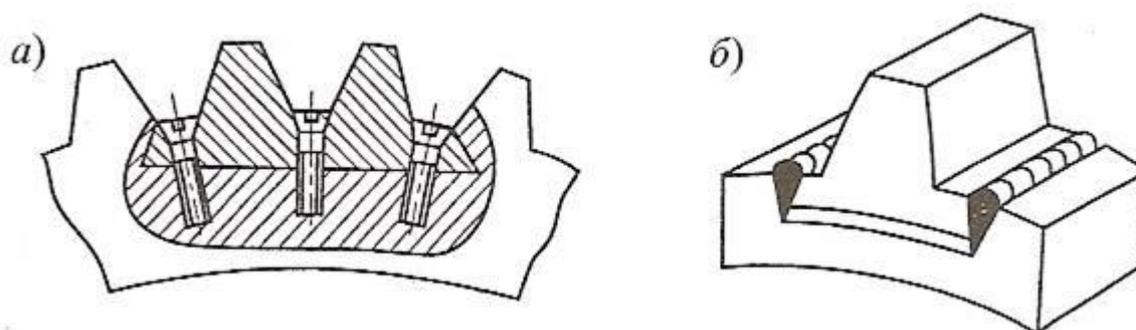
Схема ремонта зубчатого колеса при помощи: а — винта; б — сварки
